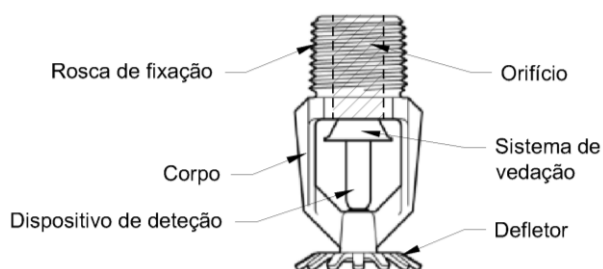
Elementos de um sprinkler (adaptado de [33])
